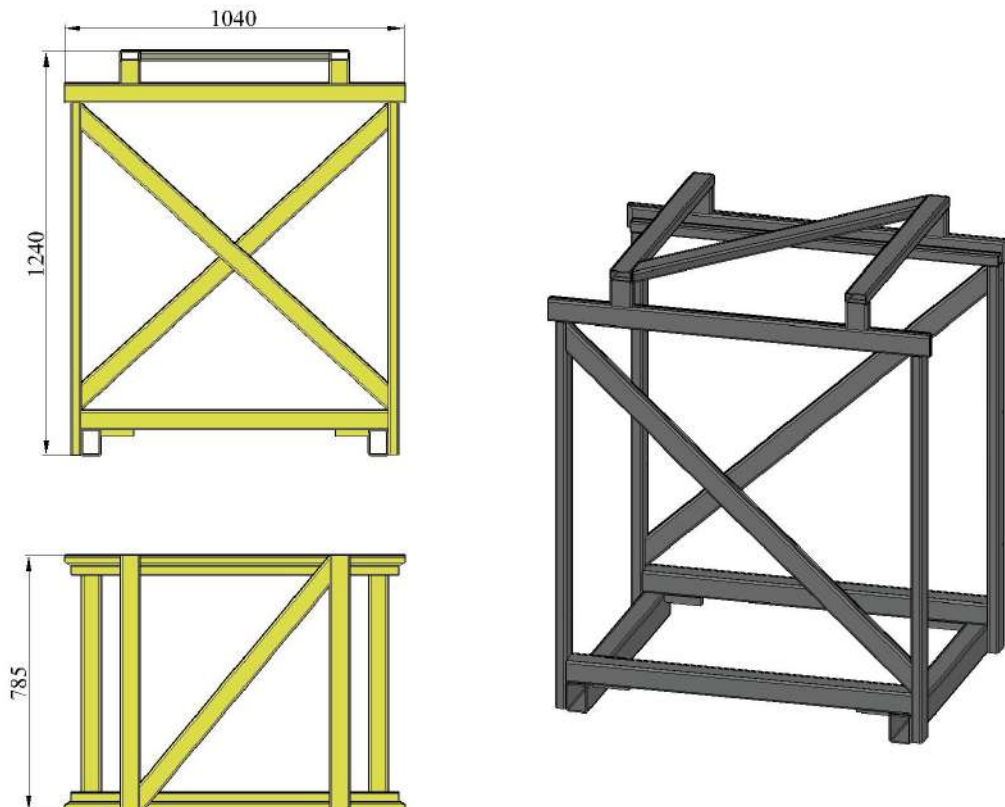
Лоток Контейнера (ЛК). Общий вид с габаритными размерами.
